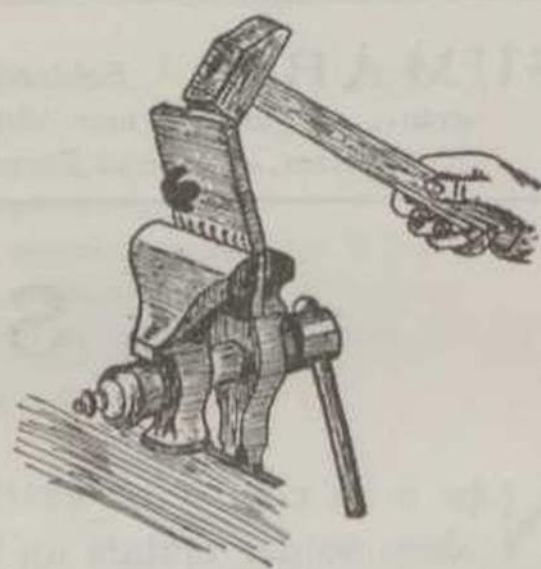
Ensáio de uma soldadura dobrando-a na linha soldada.
